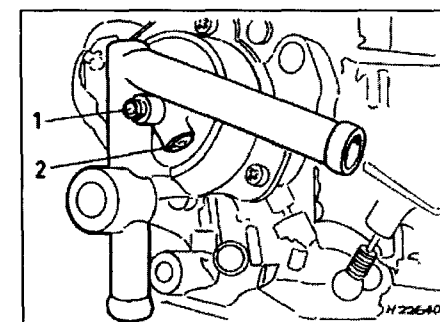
Крышка корпуса биметаллической пружины - некоторые двигатели VW
